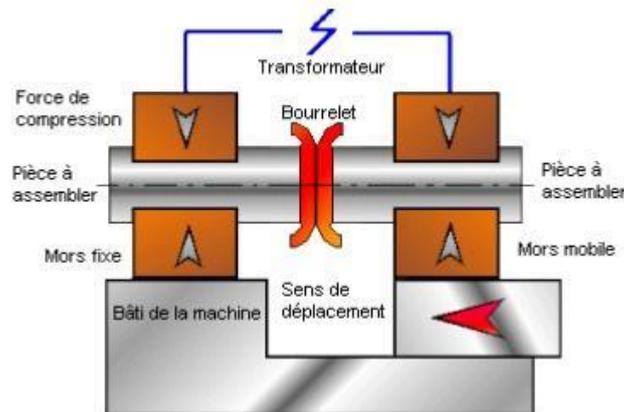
Soudage en bout par étincelage [17]
